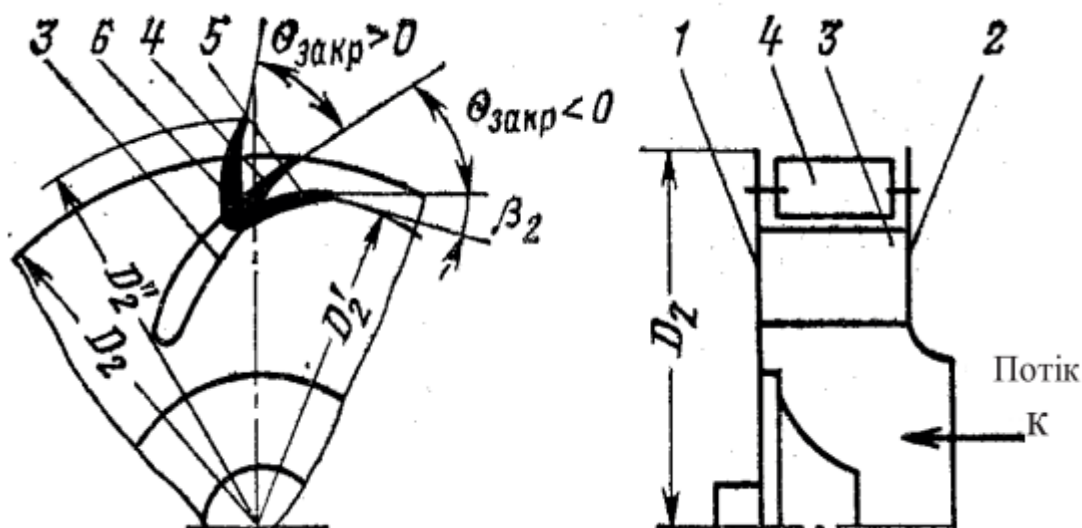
Регулювання швидкості поворотом закрилок лопаток відцентрового робочого колеса
